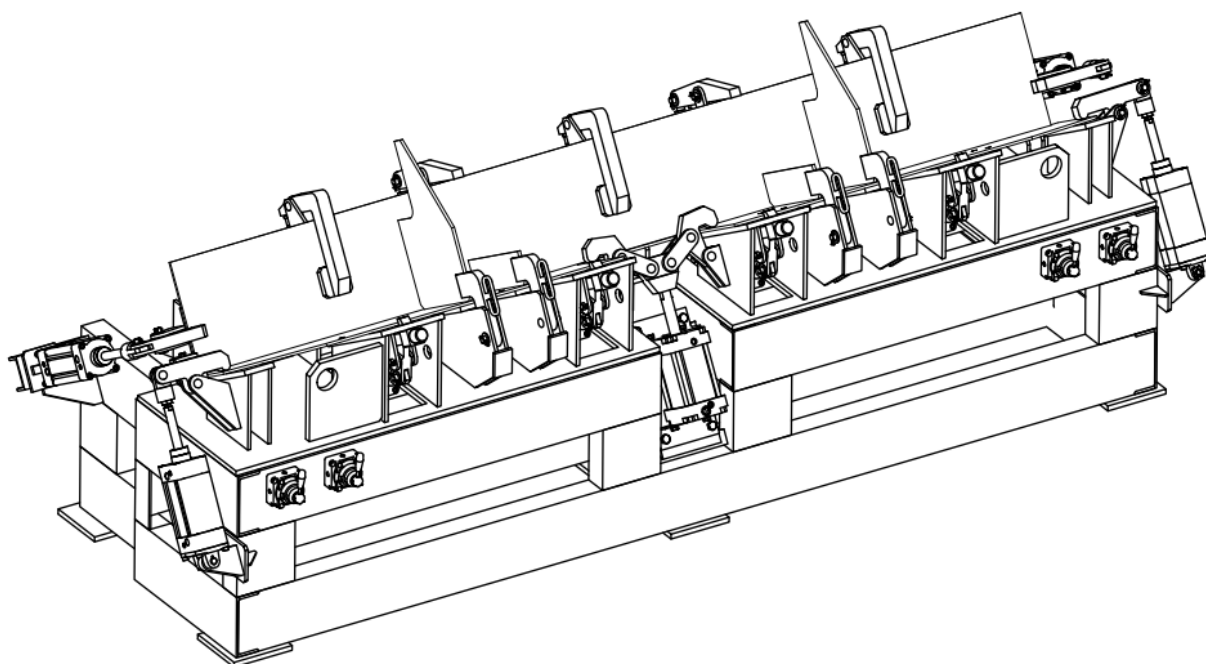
Модель станда сборки балки концевой (оснащен пневматическими прижимными устройствами. Вид спереди)
